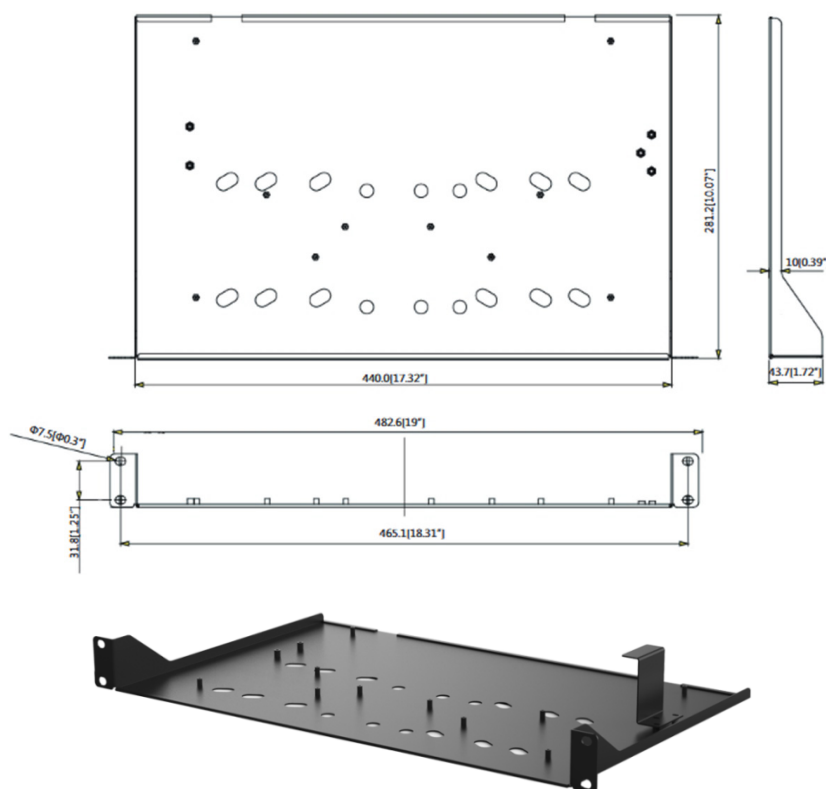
Внешний вид и габариты BOLID BR-111
